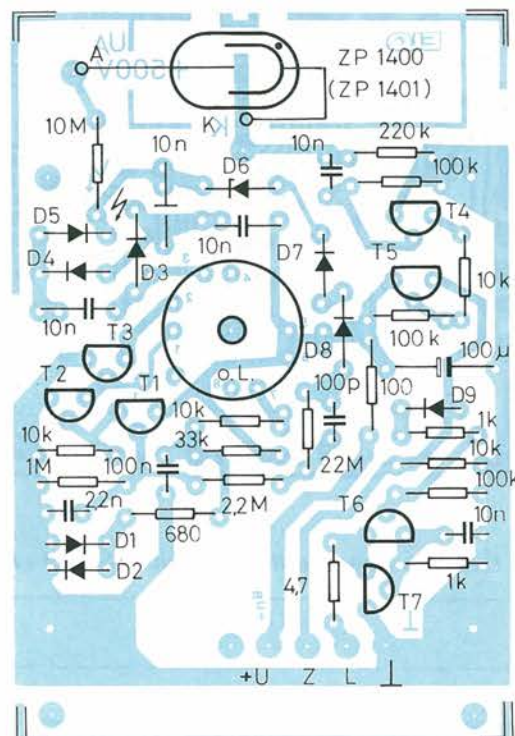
Disposizione dei componenti sul circuito stampato, dell'indicatore di radiazione.
